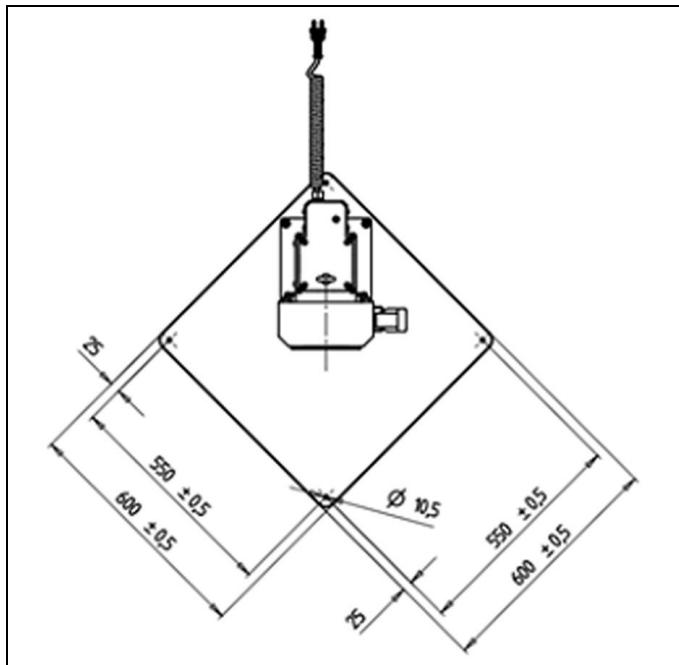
Bodenplatte mit Befestigungsbohrungen (4x Ø 10,5mm)
